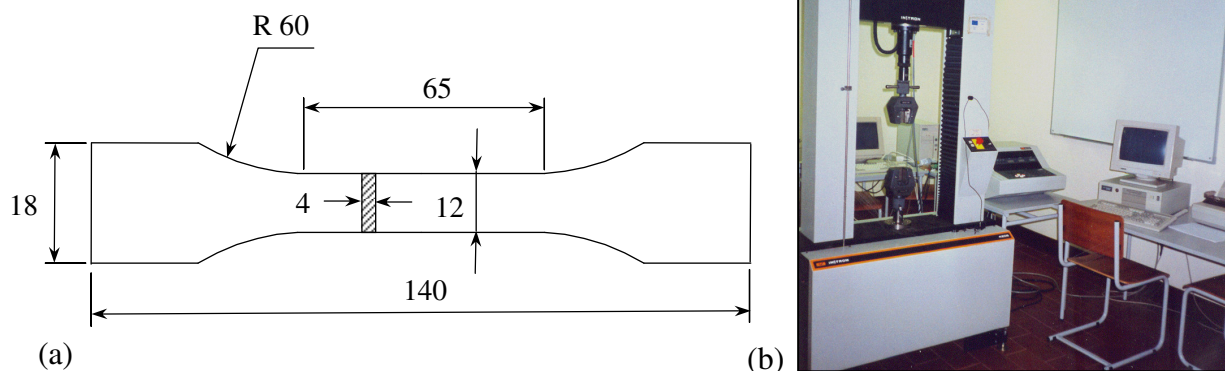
(a) Geometria e dimensões do provete (mm); (b) Máquina de ensaios de tração.
